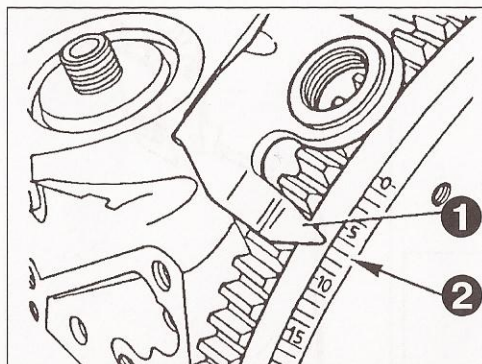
Положение начала подачи топлива на маховике двигателя.
